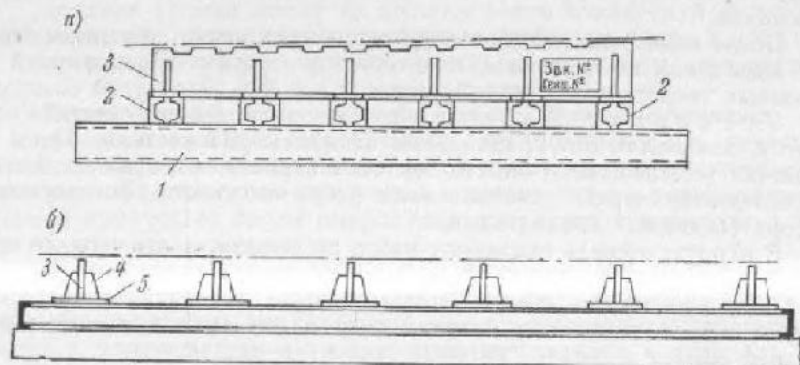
Постель для сборки бортовой секции: а — поперечное сечение; б — вид сбоку.
